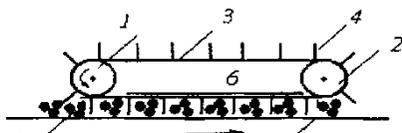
Сжатия скребкового транспортера: 1- механизм привода цепной передачи; 2 — механизм натяжения цепной передачи; 3 - бесконечная цепная передача; 4 - скребок; 5 - опорная поверхность продукта; б - опорная поверхность цепной передачи; 7 - продукт
